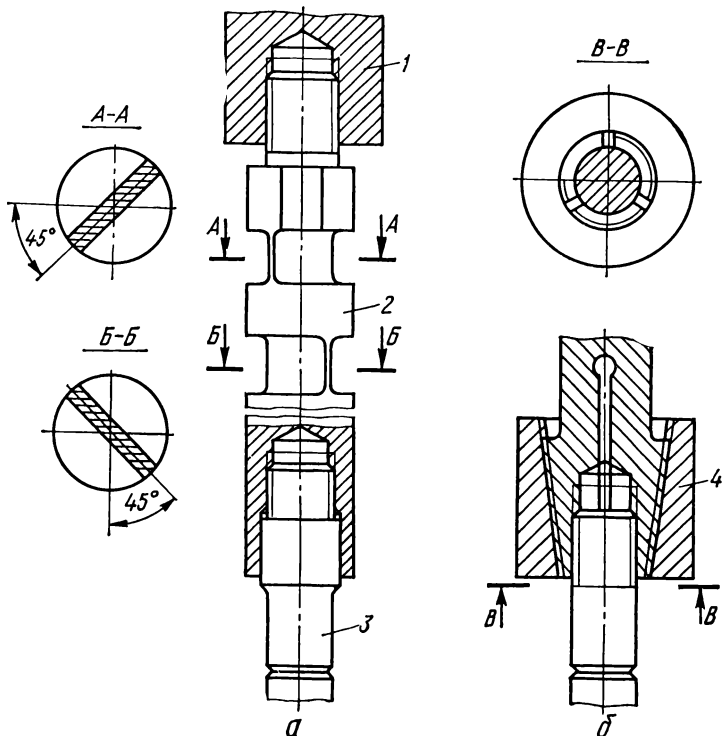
Приспособление для крепления цилиндрических образцов на растяжение (Ц — К — Р) в двух вариантах — с направляющей поверхностью (а) и с разрезной цангой (б):
